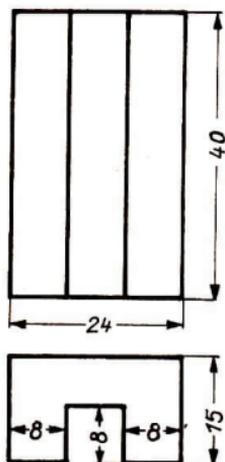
Werkstück in Vorderansicht und Draufsicht
